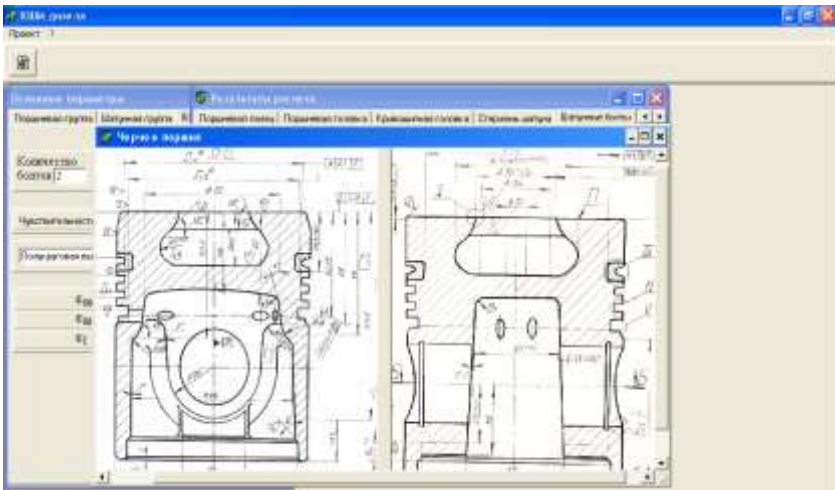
Рабочая документация для изготовления опытного образца поршня
